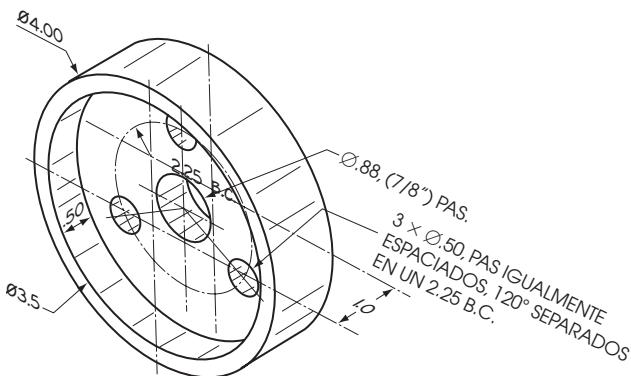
■ Soporte de columna. Dibuje las vistas necesarias, con la sección completa (Esquema A-3).
